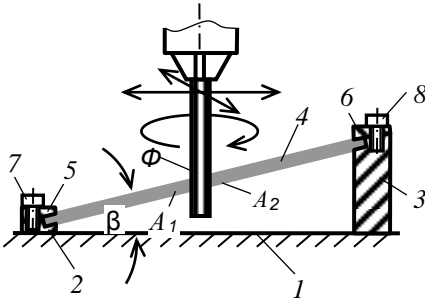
Принципова схема пристрою для встановлення заготовок на столі фрезерного верстата для виготовлення складних профілів різальних лез інструментів
